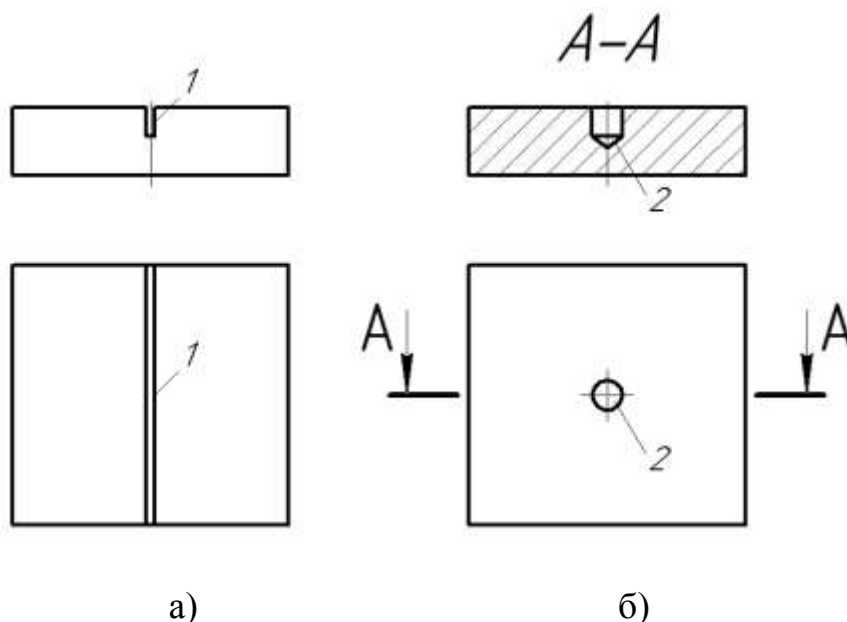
Образцы с искусственными дефектами: поверхностным пазом – а), вертикальным сверлением – б)
